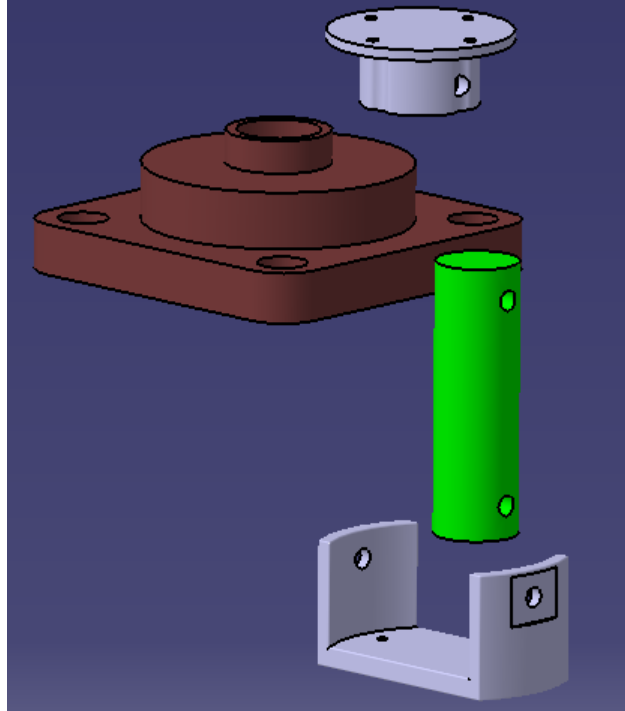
Despiece del conjunto de piezas del subensamblaje intermedio.
